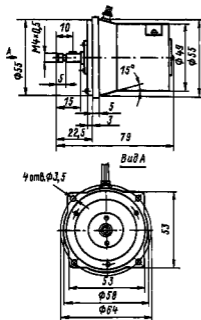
Габаритные и установочные размеры двигателя ГТ-211М
